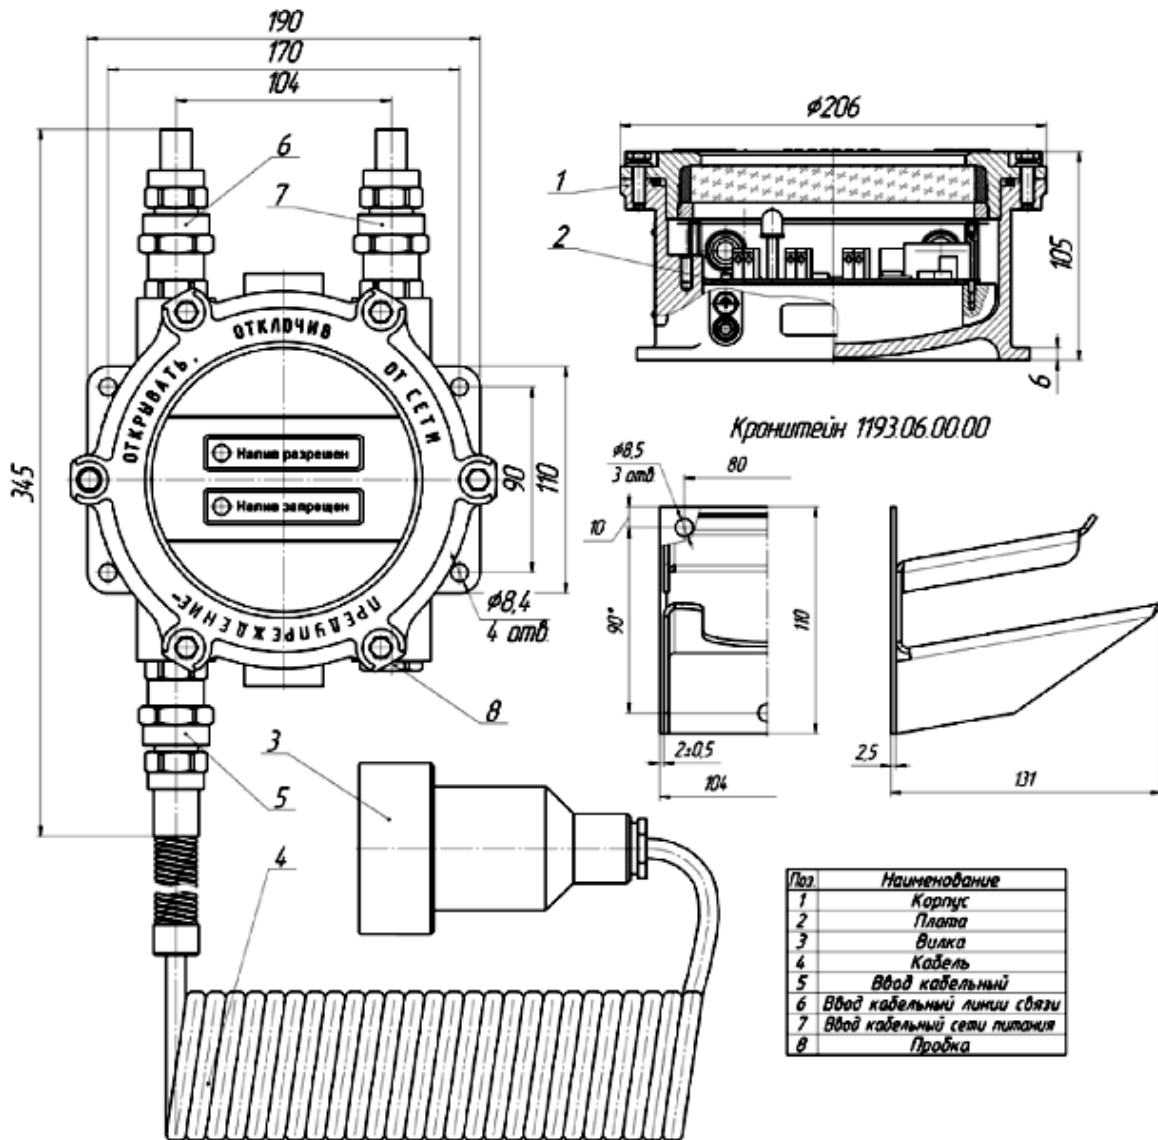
Габаритные и присоединительные размеры монитора МН-01Ех.
